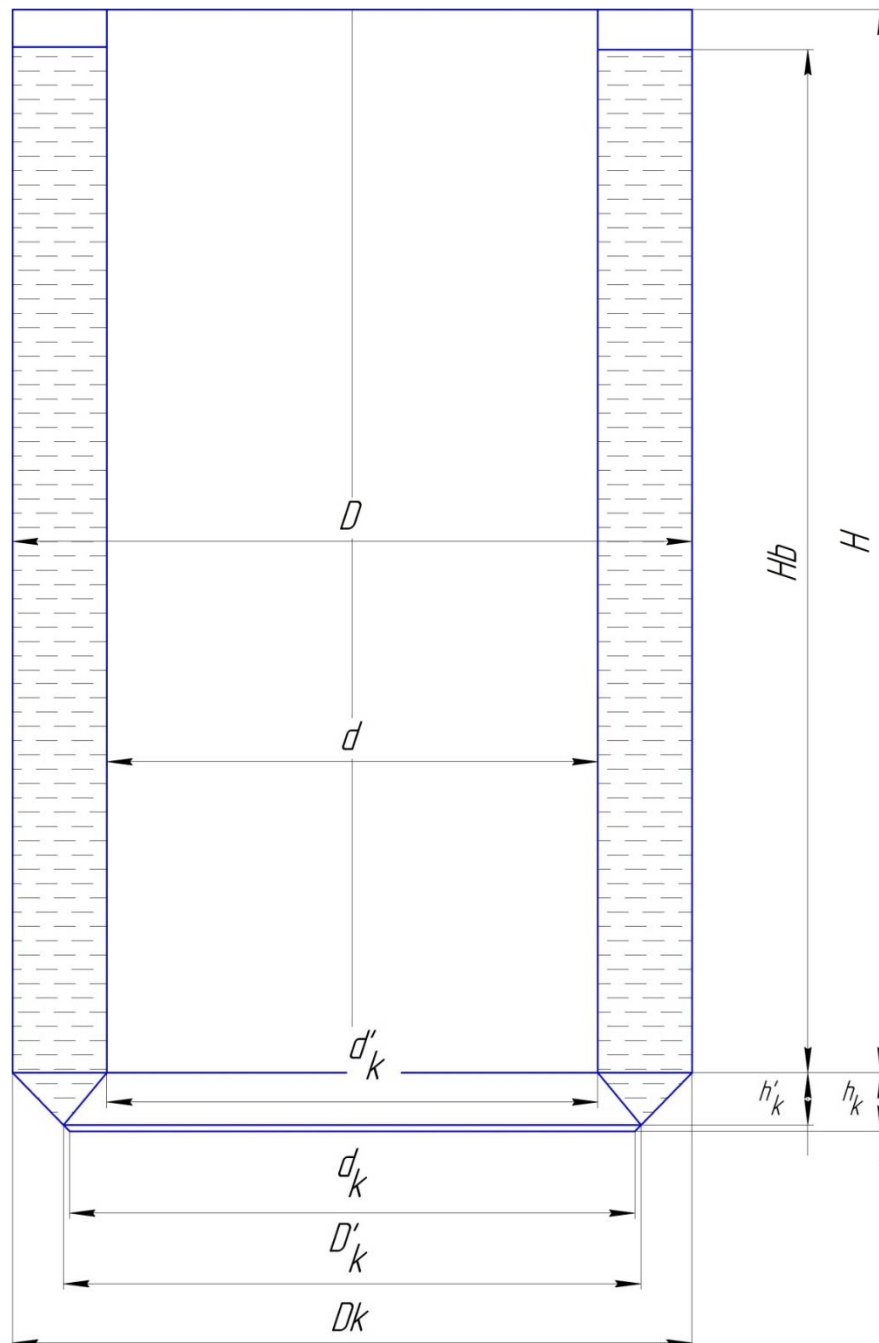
Розрахункова схема для розрахунку корпусу апарата
